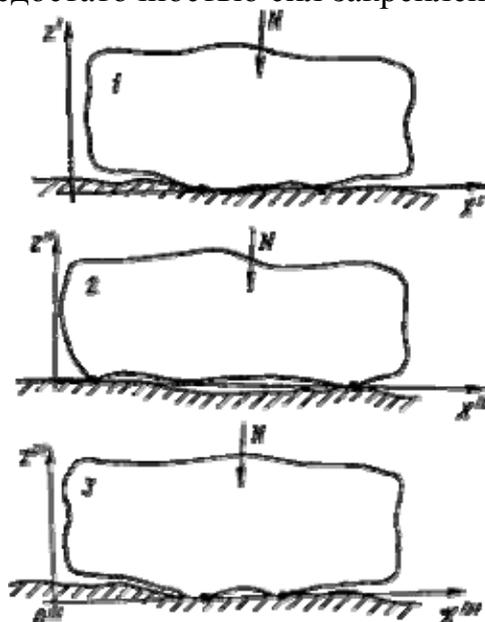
Случайное расположение точек контакта заготовки с базующими элементами станка или приспособления
